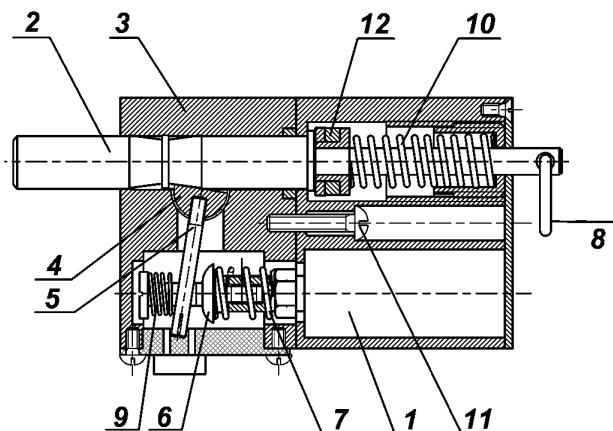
Конструкция механизма УБОП: 1 – электромагнит; 2 – шток; 3 – корпус; 4 – поворотный клин; 5 – рычаг; 6 – толкатель; 7 – пружина; 8 – кольцо; 9 – пружина; 10 – пружина возвратная; 11 – винт; 12 – кольцевой магнит
